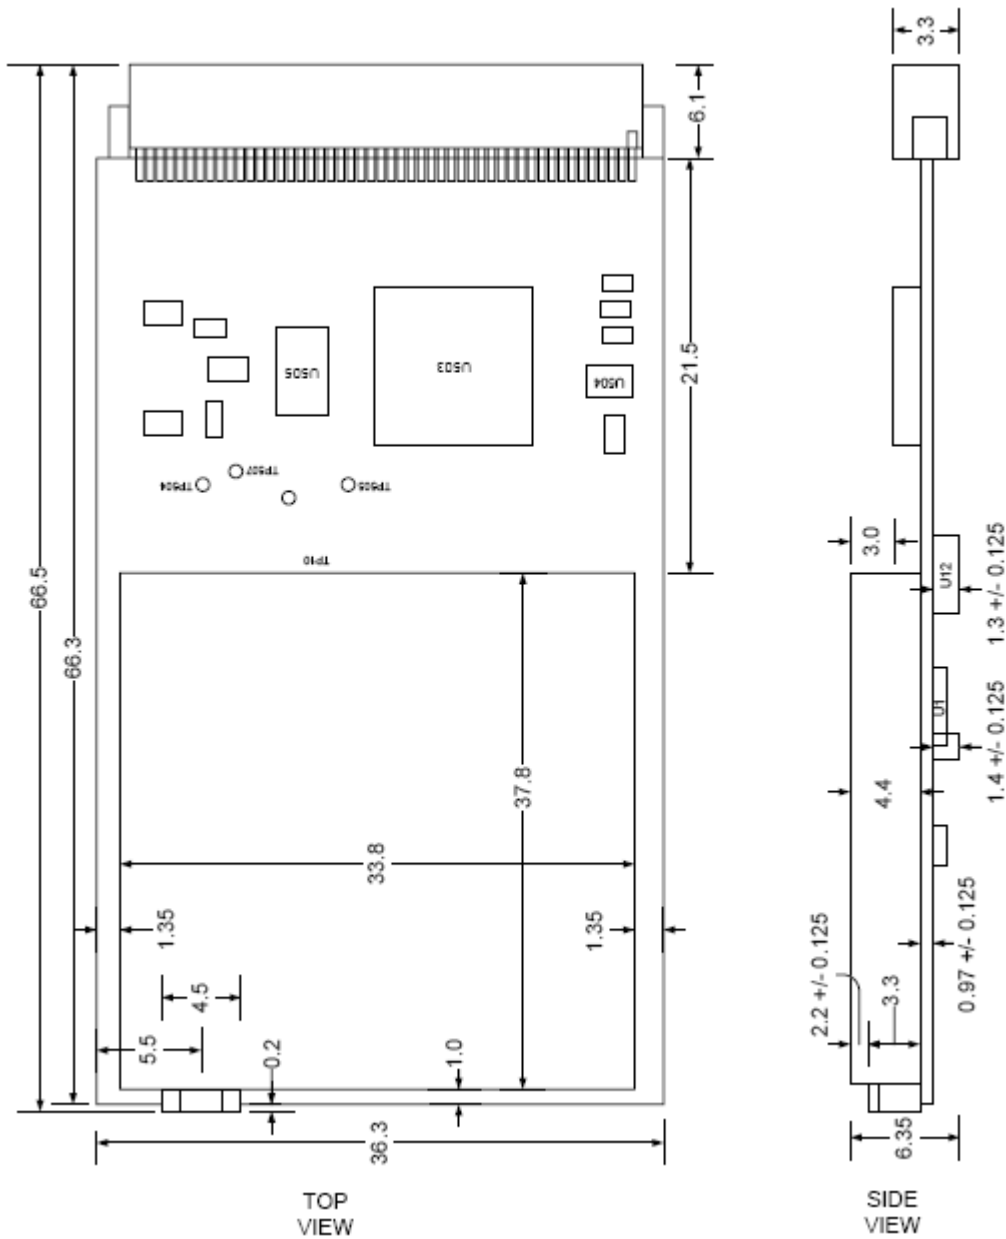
SkyModule M9 Dimensions 尺寸 (CF 卡式)
